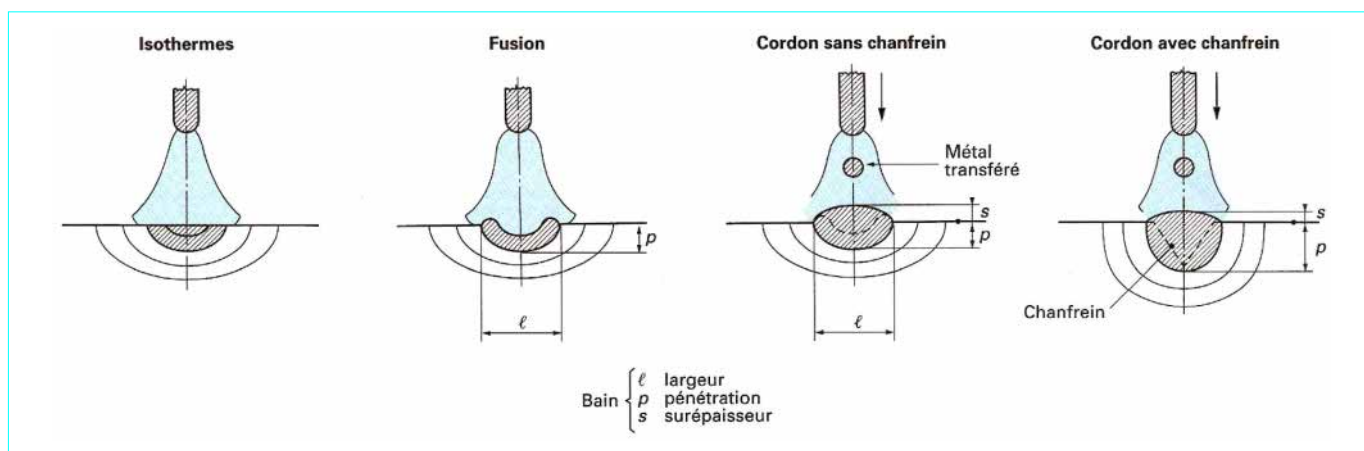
Formation de la soudure : isothermes, fusion, cordon avec ou sans chanfrein
